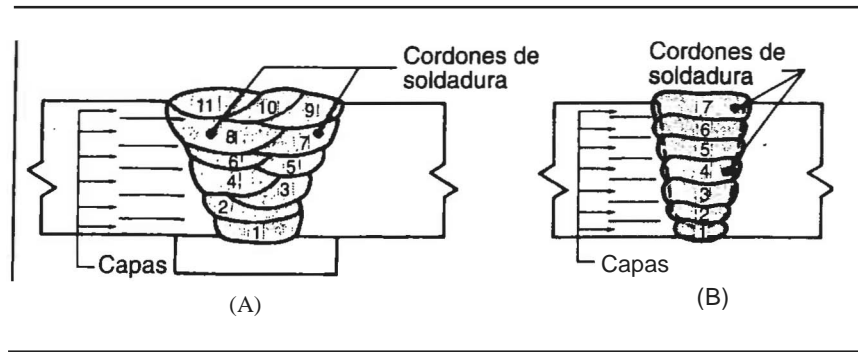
CORDONES DE SOLDADURA Y CAPAS DE SOLDADURA
